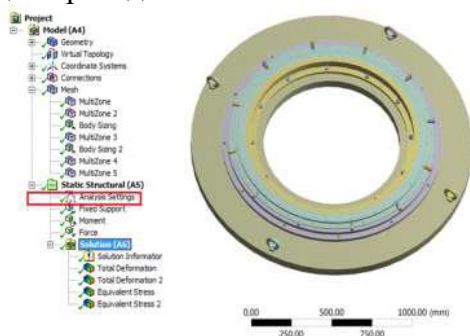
Геометрическая модель приспособления в сборе с обрабатываемой деталью
